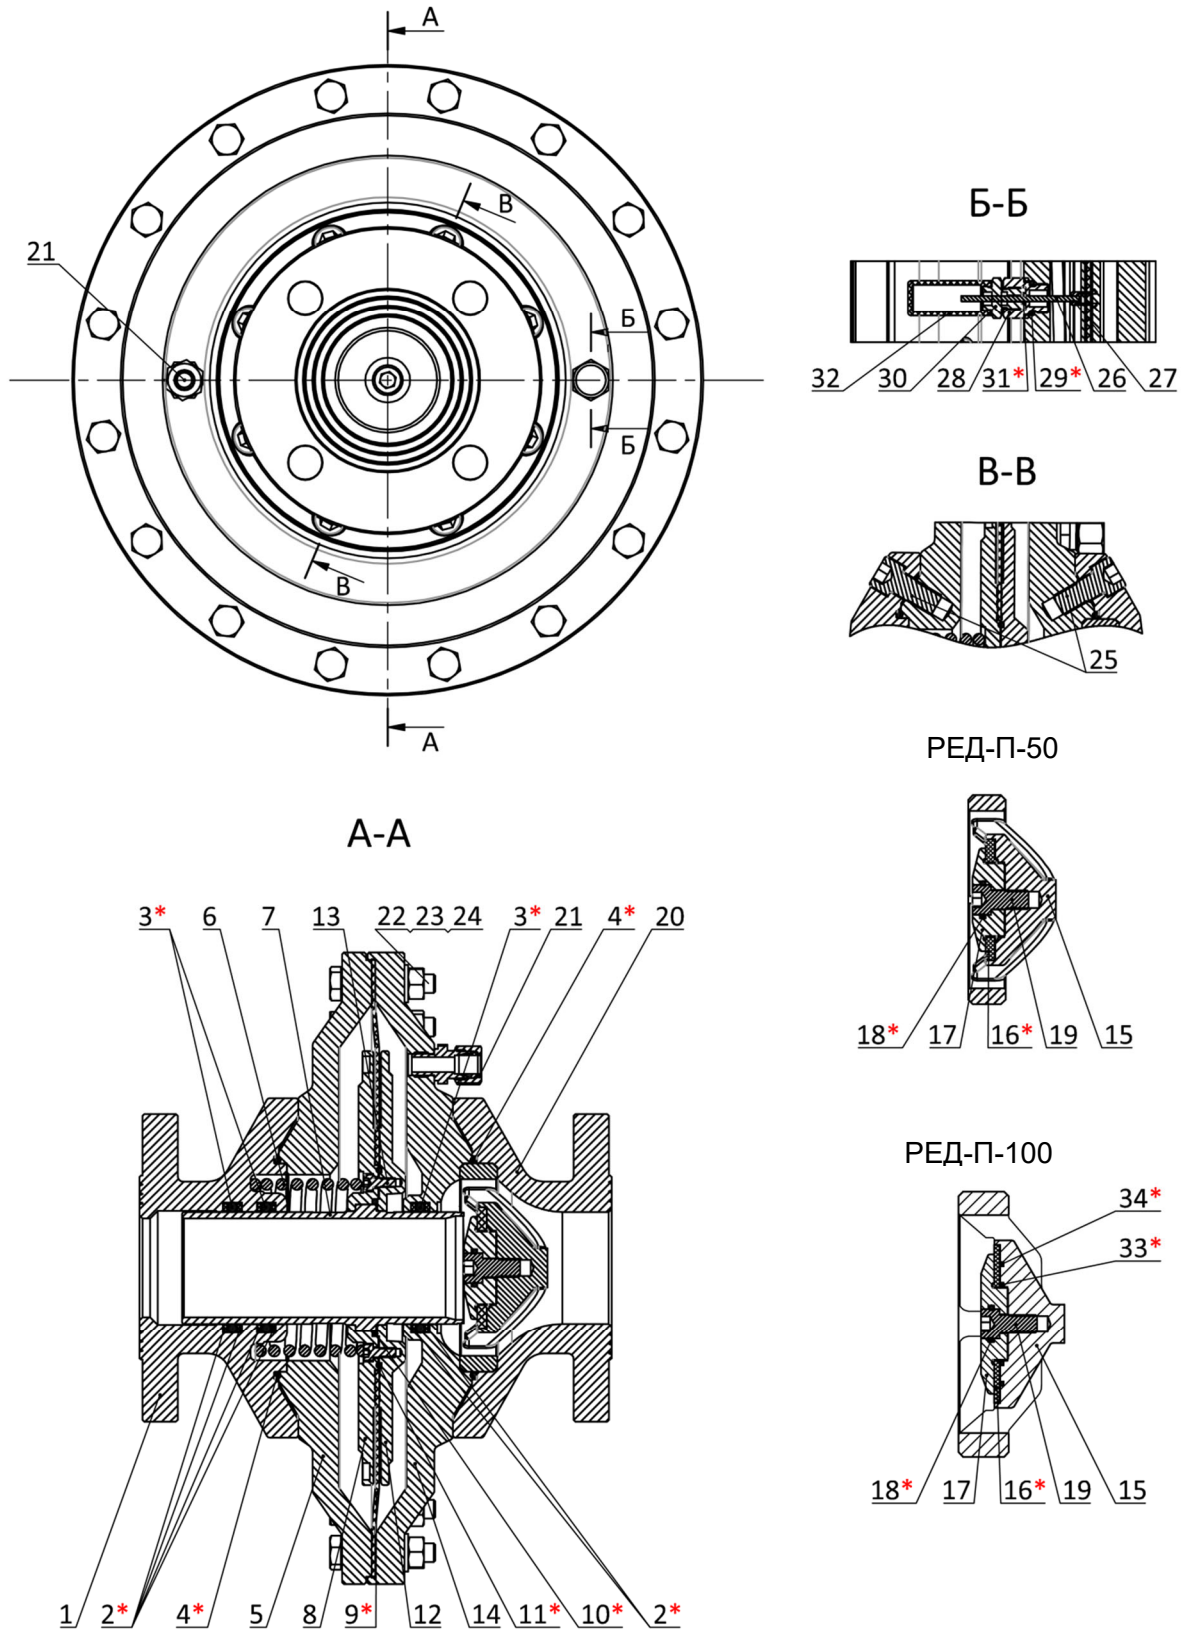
Устройство корпуса клапана предохранительного сбросного (ПСК) «РЕД-П».
